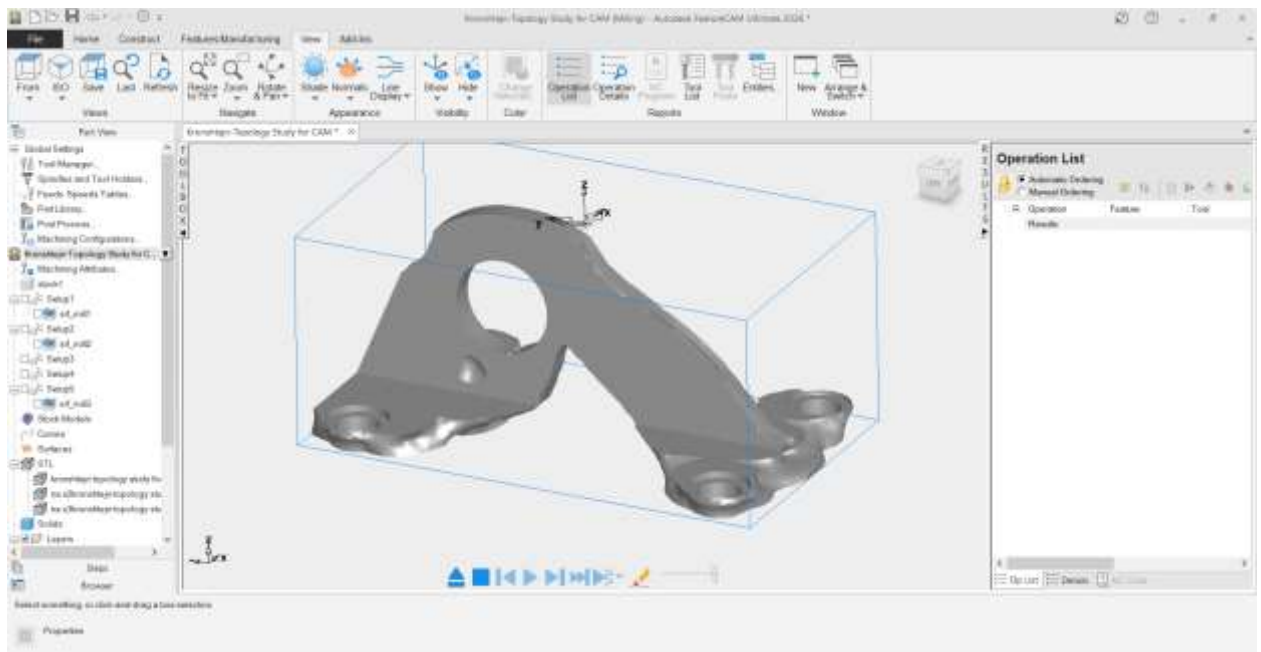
Налаштування положення деталі та форми заготовки.
